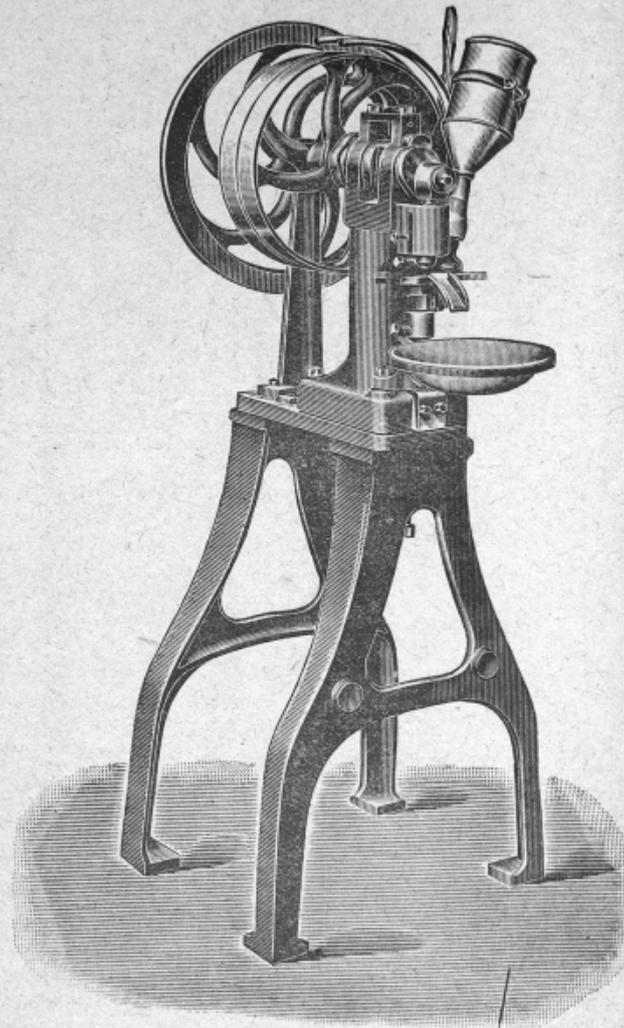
Machine à comprimer petit modèle. Pouré et Sauton.
